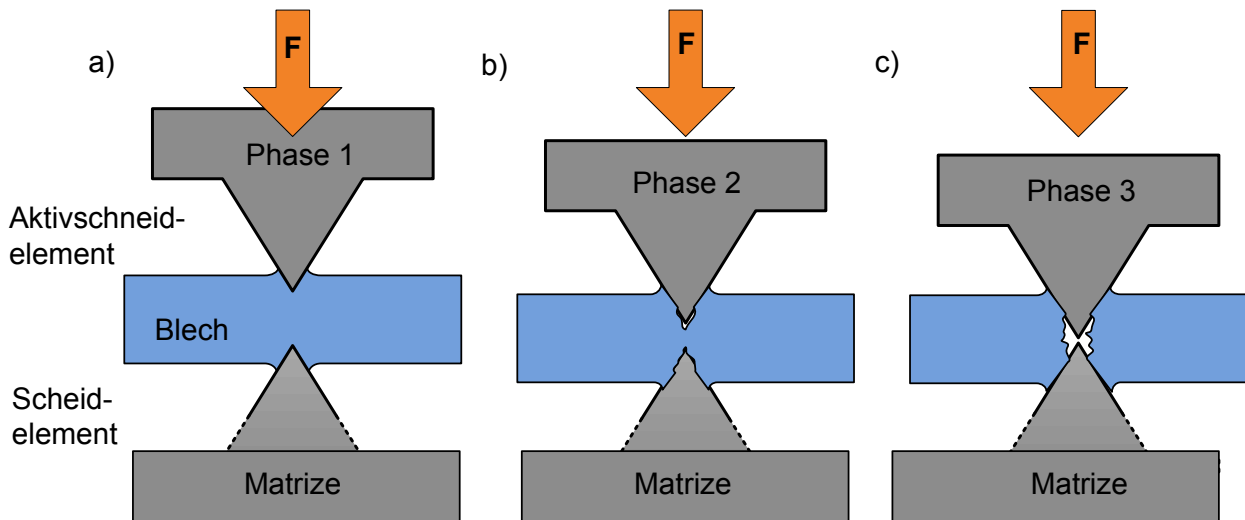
Die drei Phasen des Beißschneidens a) Eindringen; b) Rissinitierung; c) getrenntes Werkstück
